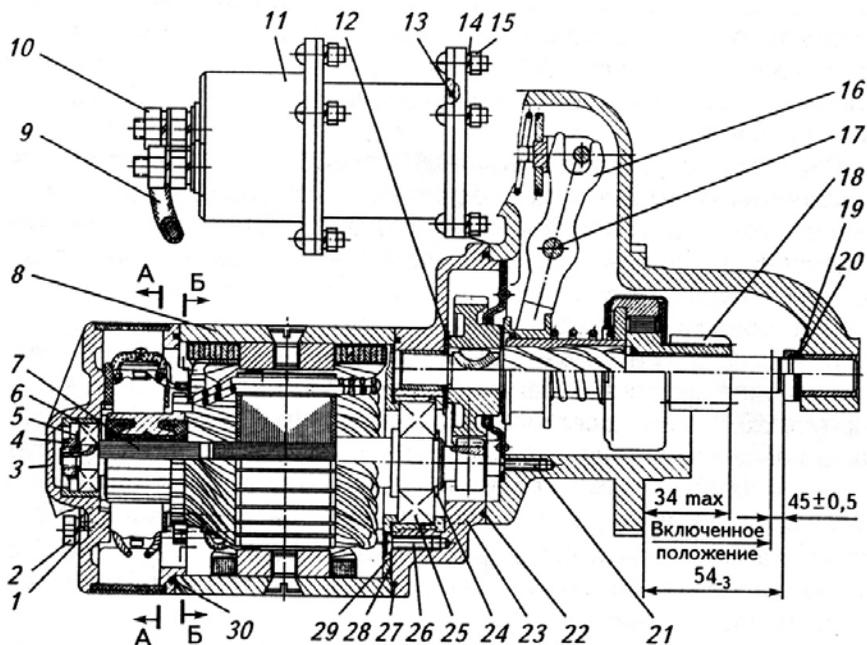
Стартер со встроенным цилиндрическим редуктором с внешним зацеплением:
